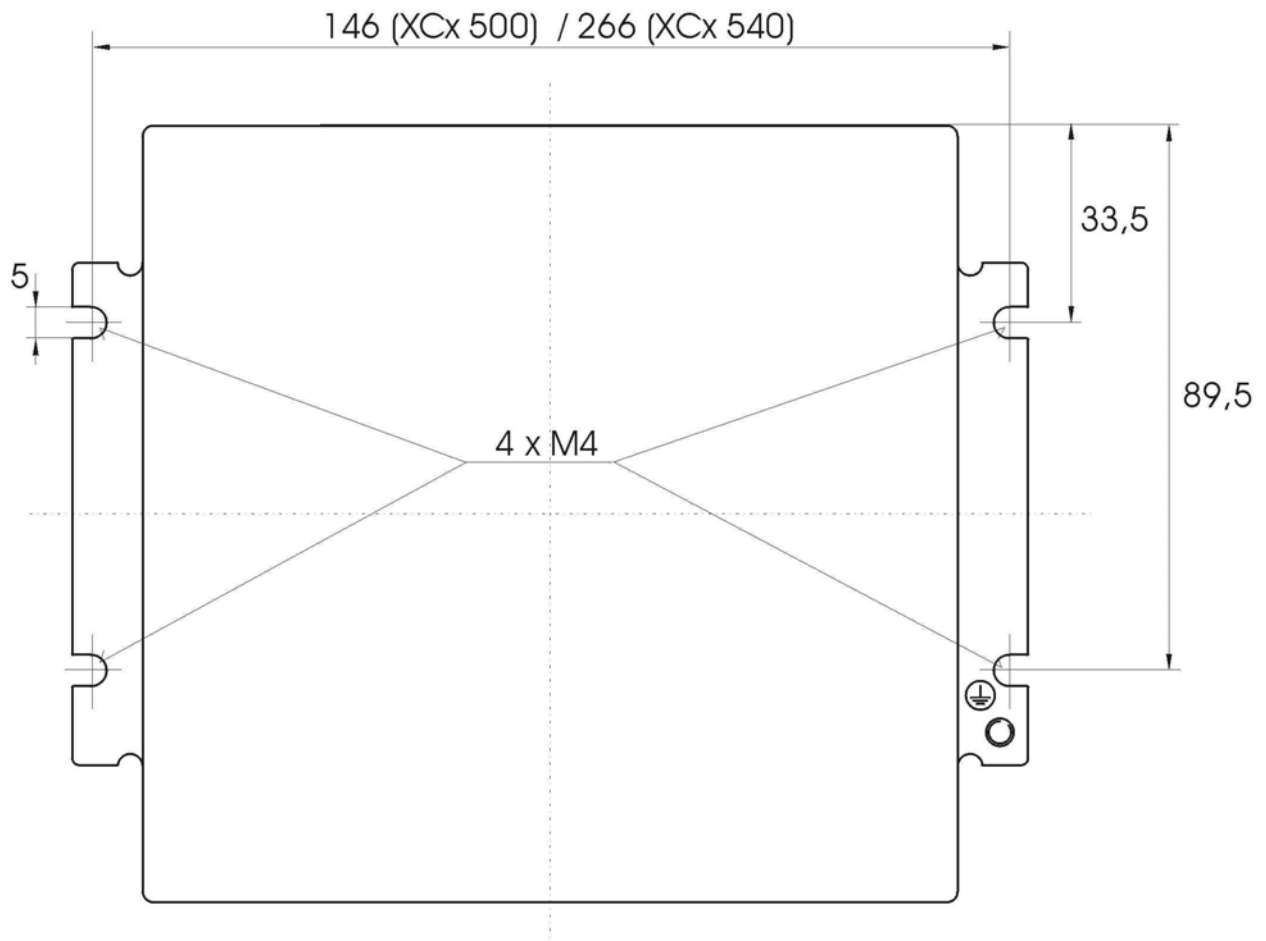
Abmaße der Befestigungslöcher für Schraubmontage der XCx 500/540
